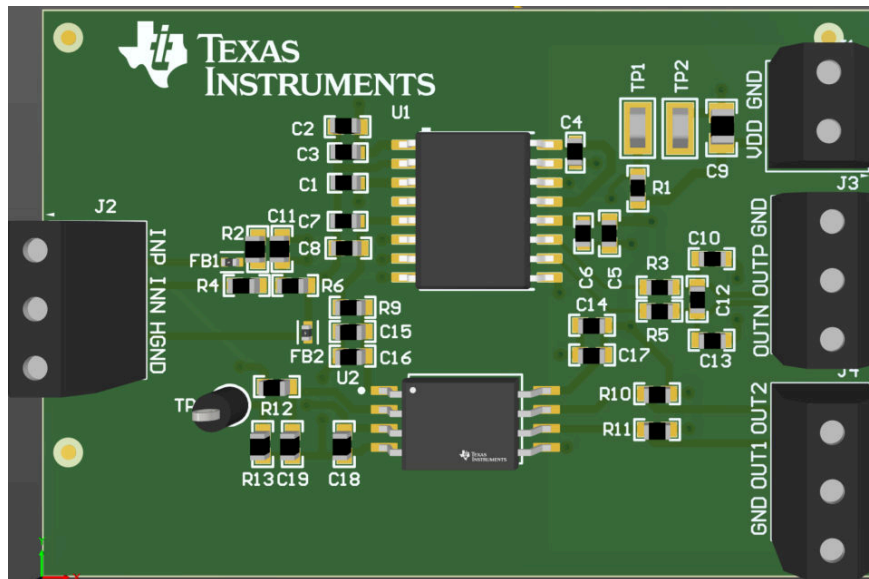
AMC3311 및 AMC23C11 PCB 레이아웃
